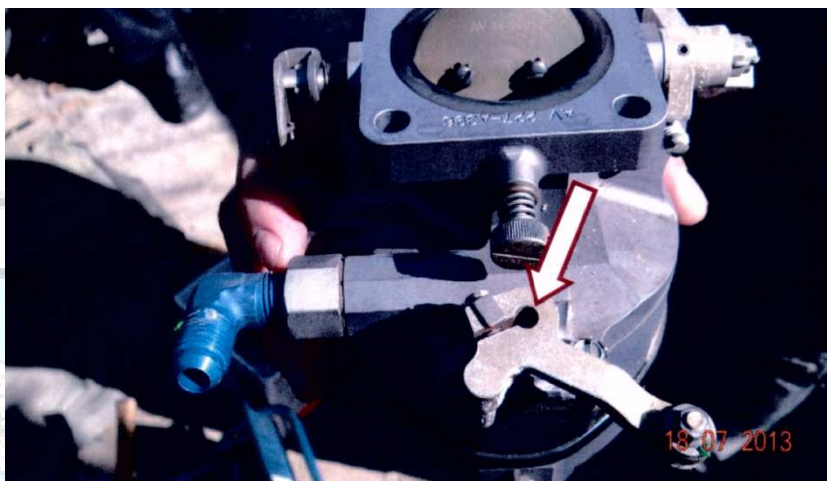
Vista da alavanca montada no carburador. Observa-se que a extremidade da haste da válvula não está visível.
